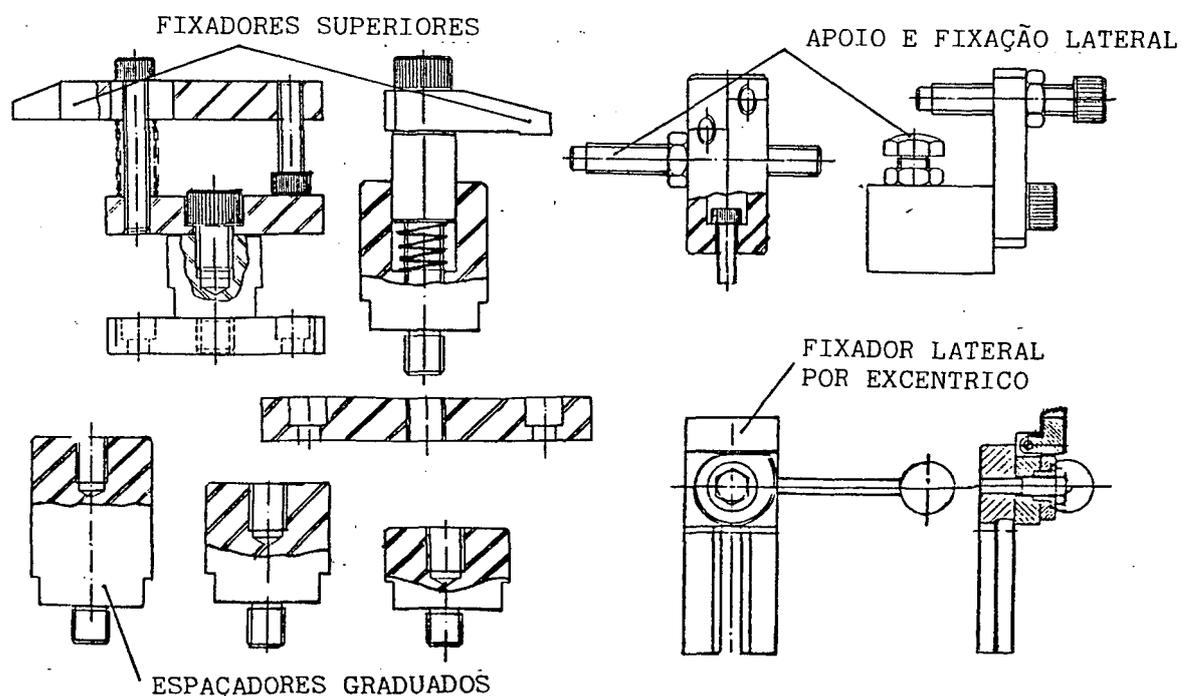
Elementos de fixação de peças de diversos perfis geométricos [75].
